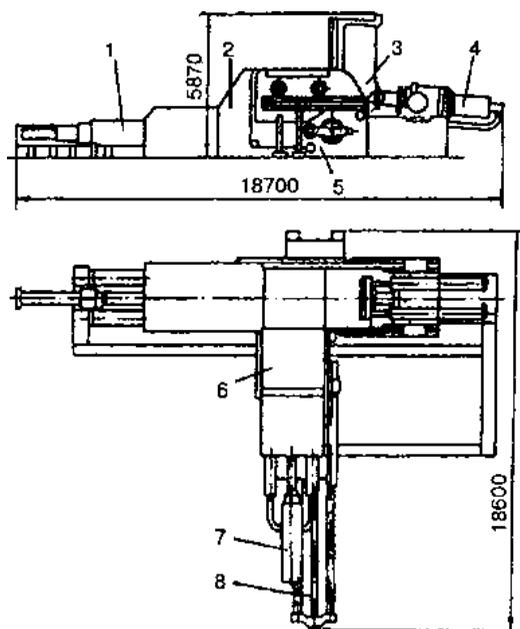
Пакетировочный гидравлический пресс Б 1642
